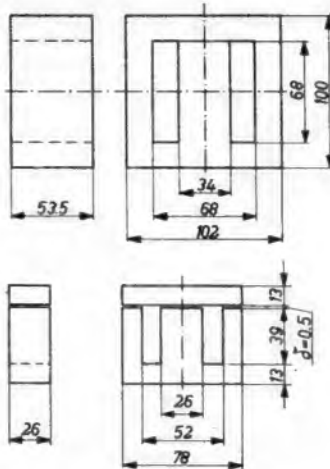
Oben: Kernabmessungen des Transformators Unten: Kernabmessungen der Drossel L
